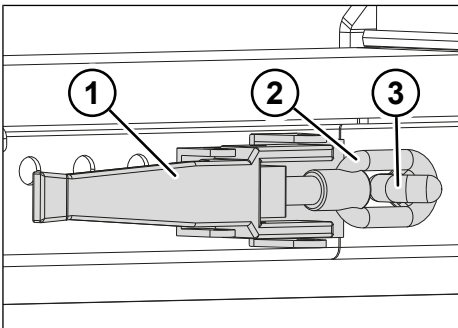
Levier de fermeture sur la poutre d'appui bloqué
